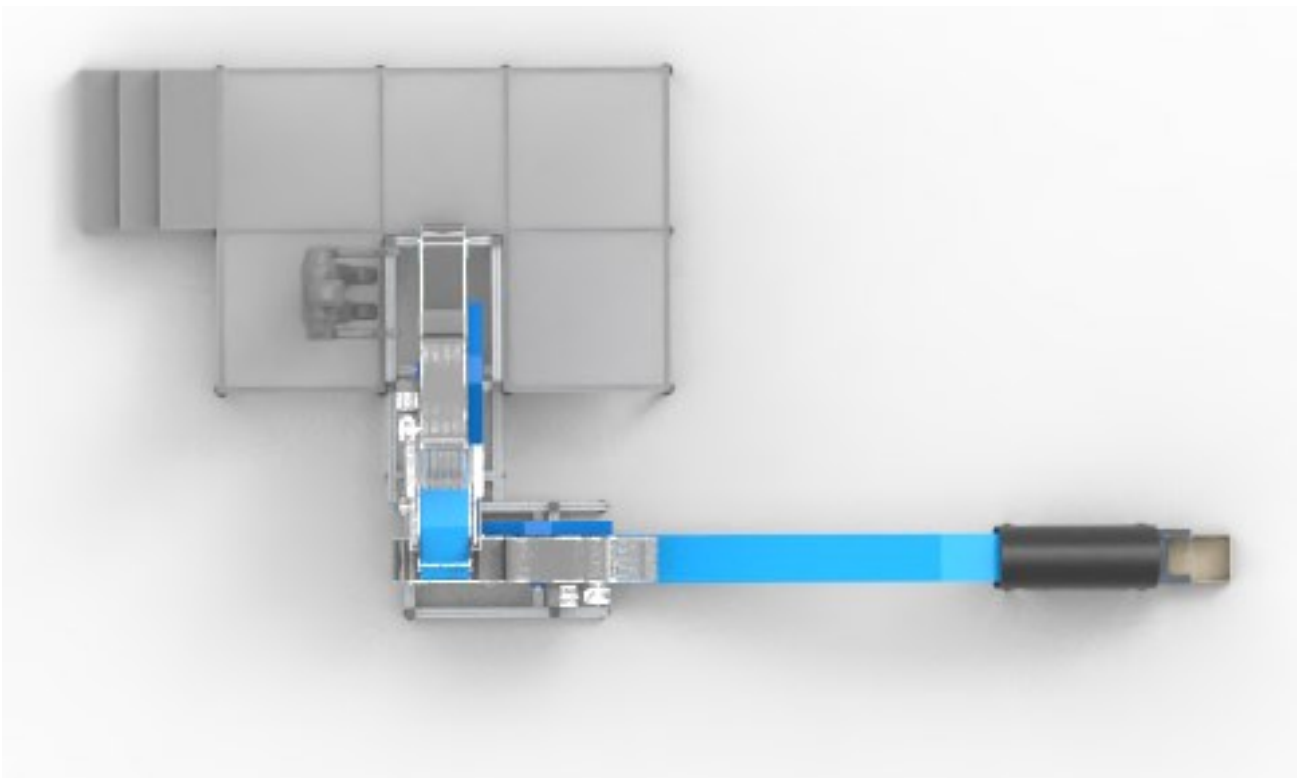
Layout complessivo del blocco 1 (vista dall'alto)
